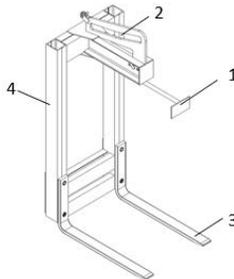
Захватное устройство для поддонов: 1 – упор; 2 – каретка; 3 – вилы; 4 – рама
